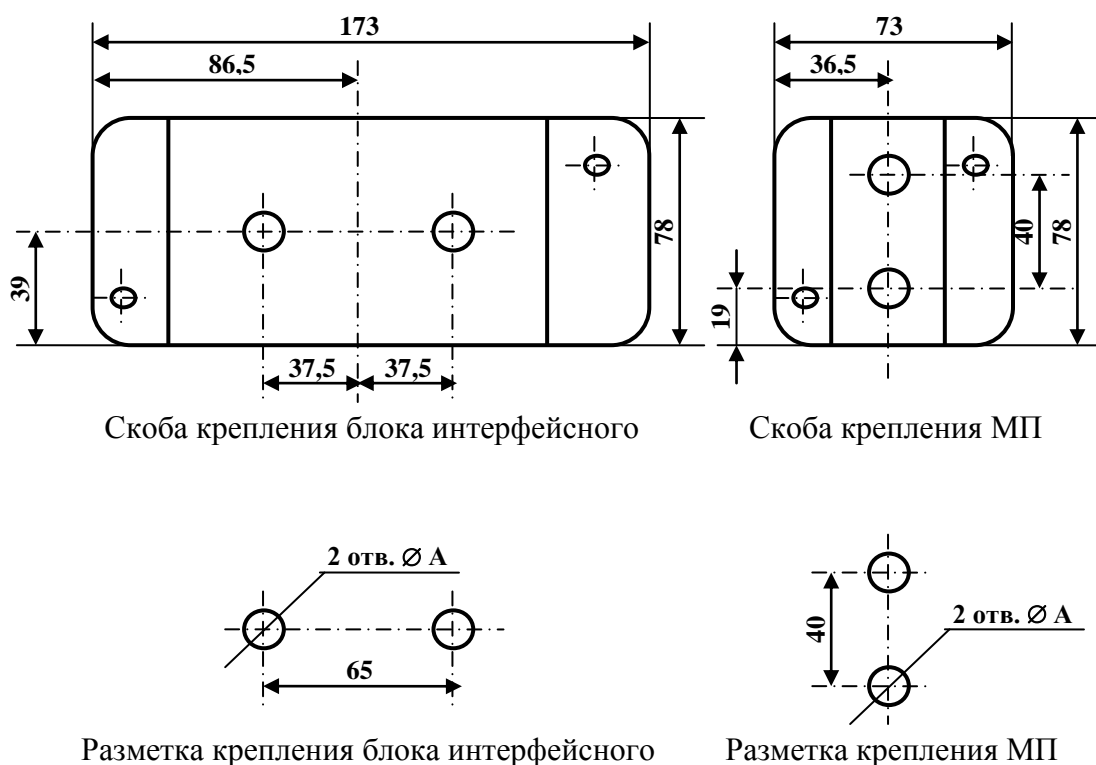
Разметка и габаритные размеры скоб крепления БИ и МП.
